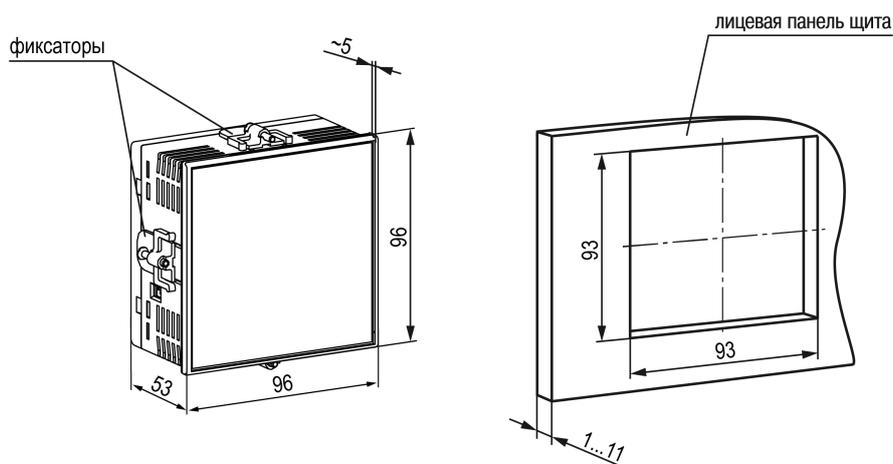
Габаритные размеры корпуса Щ1 и монтажного отверстия в щите
